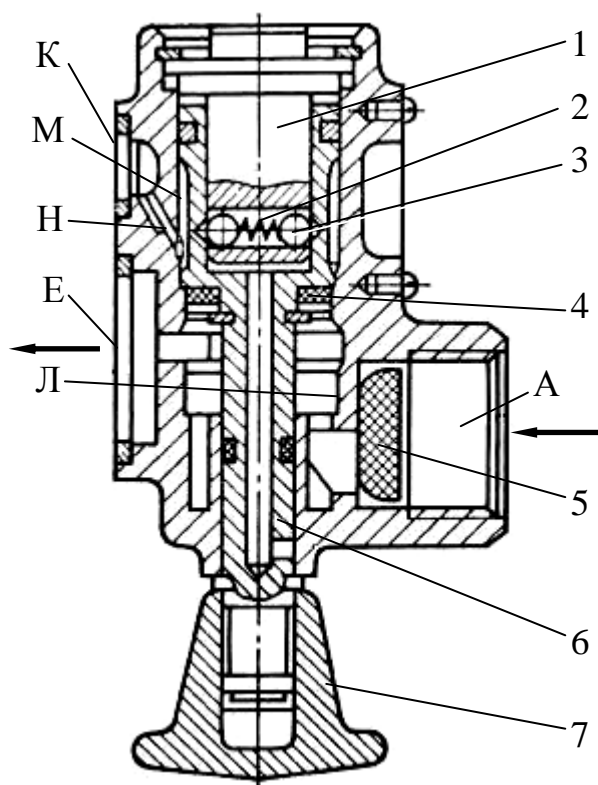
Конструкция крана растормаживания пневматического тормозного привода прицепа КАМАЗ: 1 – упор с фиксатором; 2 – пружина; 3 – шарик фиксатора; 4 – уплотнение; 5 – сетчатый фильтр; 6 – шток; 7 – рукоятка крана; А – вывод в соединительную или питающую магистраль; Е – вывод под верхний поршень воздухораспределителя; К – вывод из полости над верхним поршнем воздухораспределителя; Л – цилиндрическая поверхность; М – кольцевая проточка штока; Н – канал
